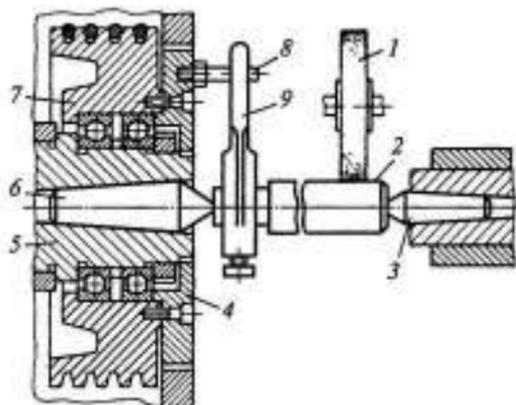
Установка заготовки в неподвижных центрах круглошлифовального станка:
